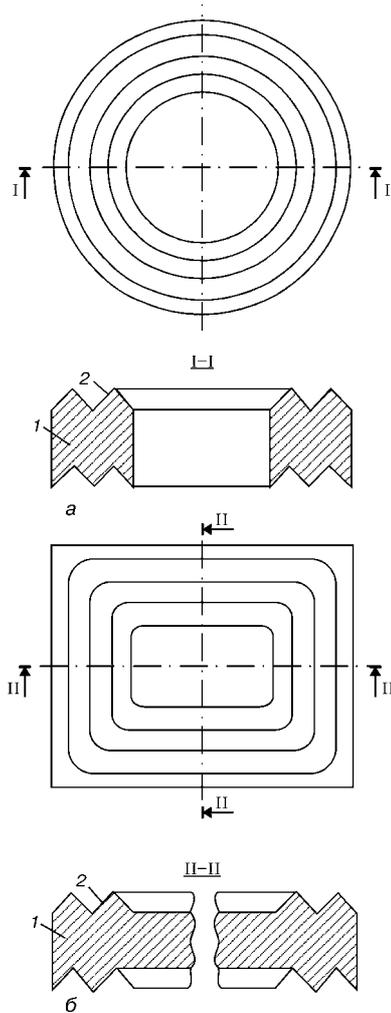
Схема профилированного нагревательного инструмента для цилиндрических деталей (а) и изделия прямоугольного сечения (б): 1 – нагревательный инструмент; 2 – адгезионный слой
